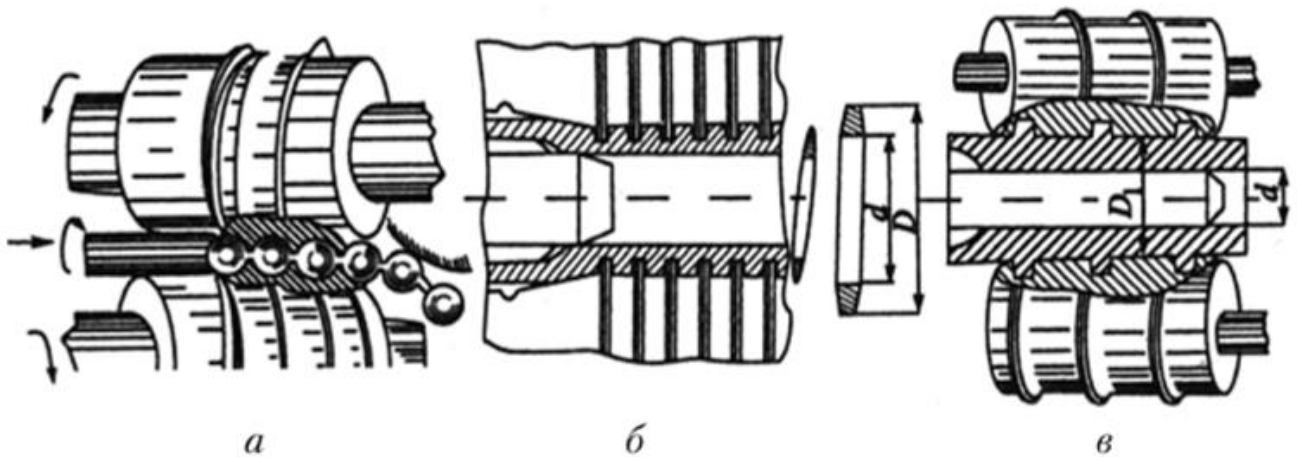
Схема отримання поковок поперечно-гвинтовою прокаткою: а - кулі; б - кільцевих поковок; в - профільованих труб
